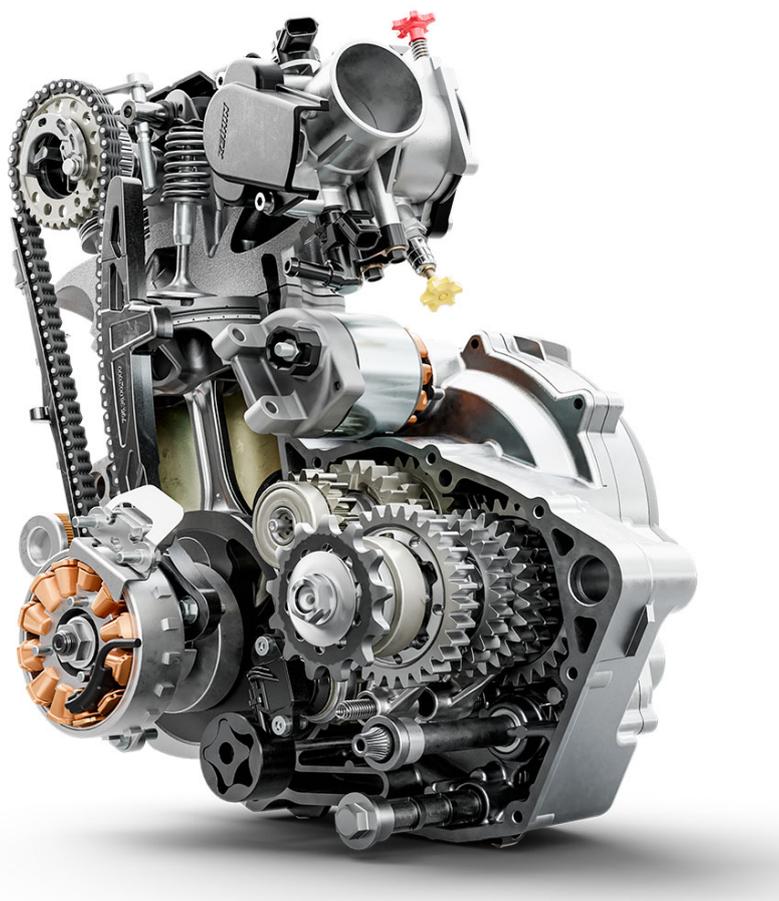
Одноцилиндровый двигатель KTM 390
